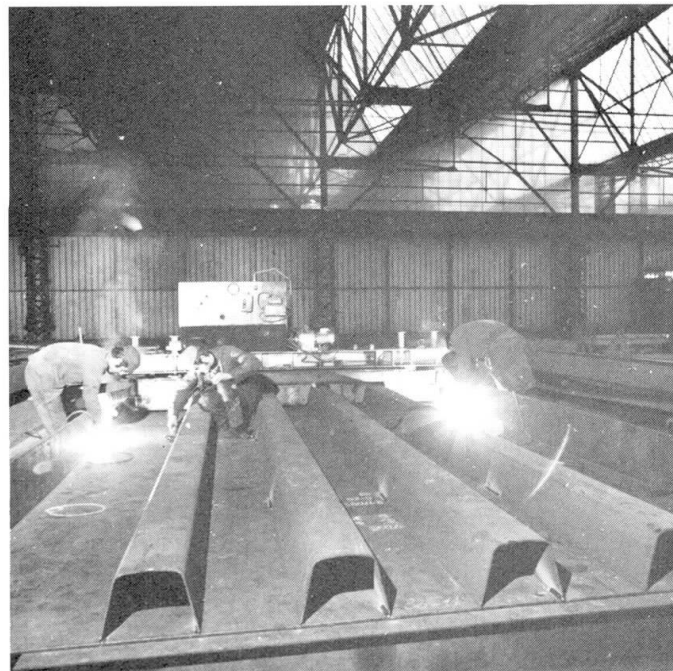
Portique de soudage des longerons de la dalle orthotrope
